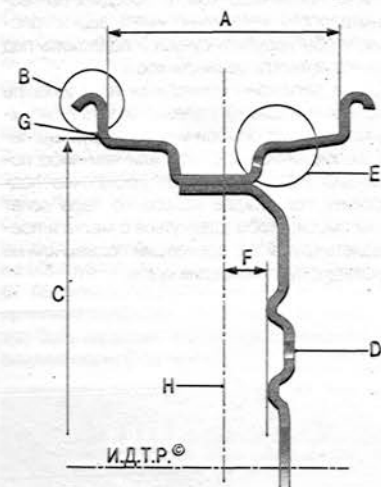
Параметры колесных дисков: А – ширина профиля обода (в дюймах); В – форма бортовой закраины обода; С – диаметр обода (в дюймах); D – количество отверстий под шпильки крепления колеса; E – профиль борта покрышки; F – вылет ET (в мм); G – точка, в которой измеряется максимальное биение диска; H – центр диска
